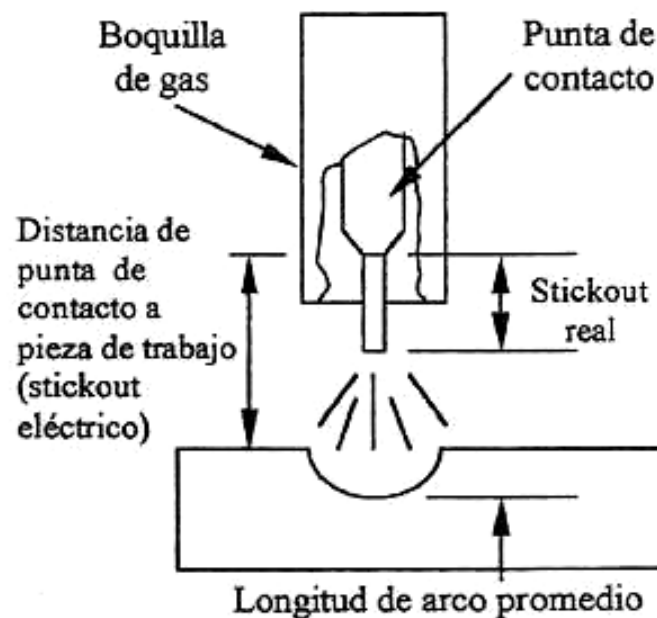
EXTENSIÓN DEL ELECTRODO
